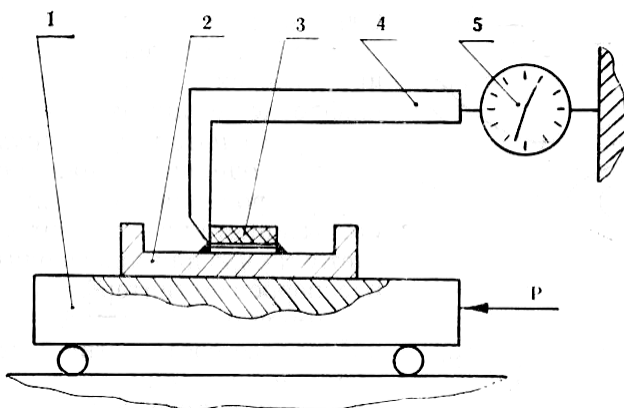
Схема контроля прочности присоединения кристалла: 1 – кристалл; 2 – корпус прибора; 3 – подвижная каретка; 4 – зацеп; 5 – динамометр
